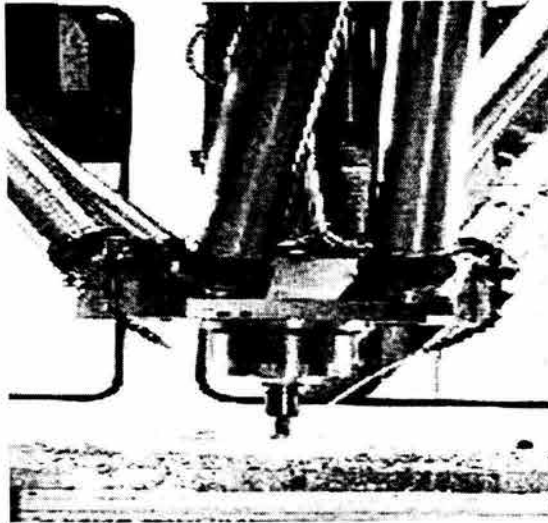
Robot Hexapod de juntas universales en un centro de maquinado.
